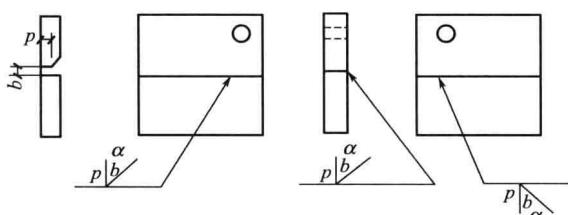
一个焊件带坡口的焊缝标注方法
